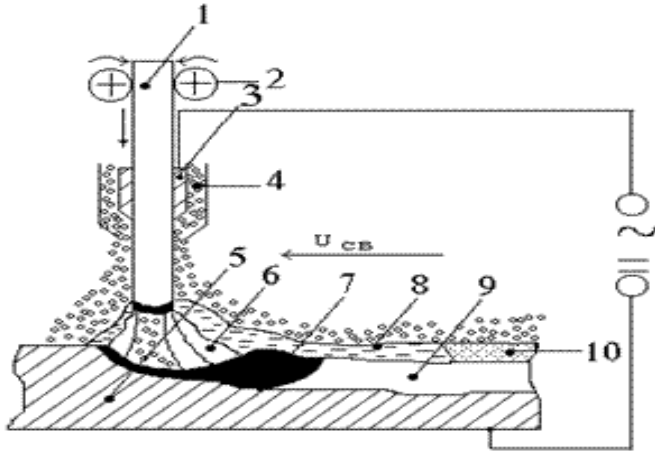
Схема автоматической сварки под флюсом: 1 – сварочная проволока; 2 – механизм подачи проволоки; 3 – скользящий контакт; 4 – флюс; 5 – основной металл; 6 – электрическая дуга; 7 – металлическая ванна; 8 – расплавленный флюс; 9 – наплавленный металл; 10 – шлаковая корка.
